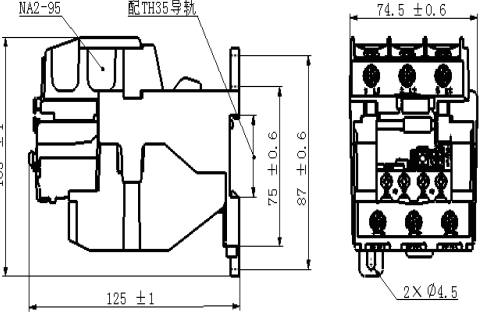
NDR2-95 带独立安装座外形尺寸与安装尺寸
